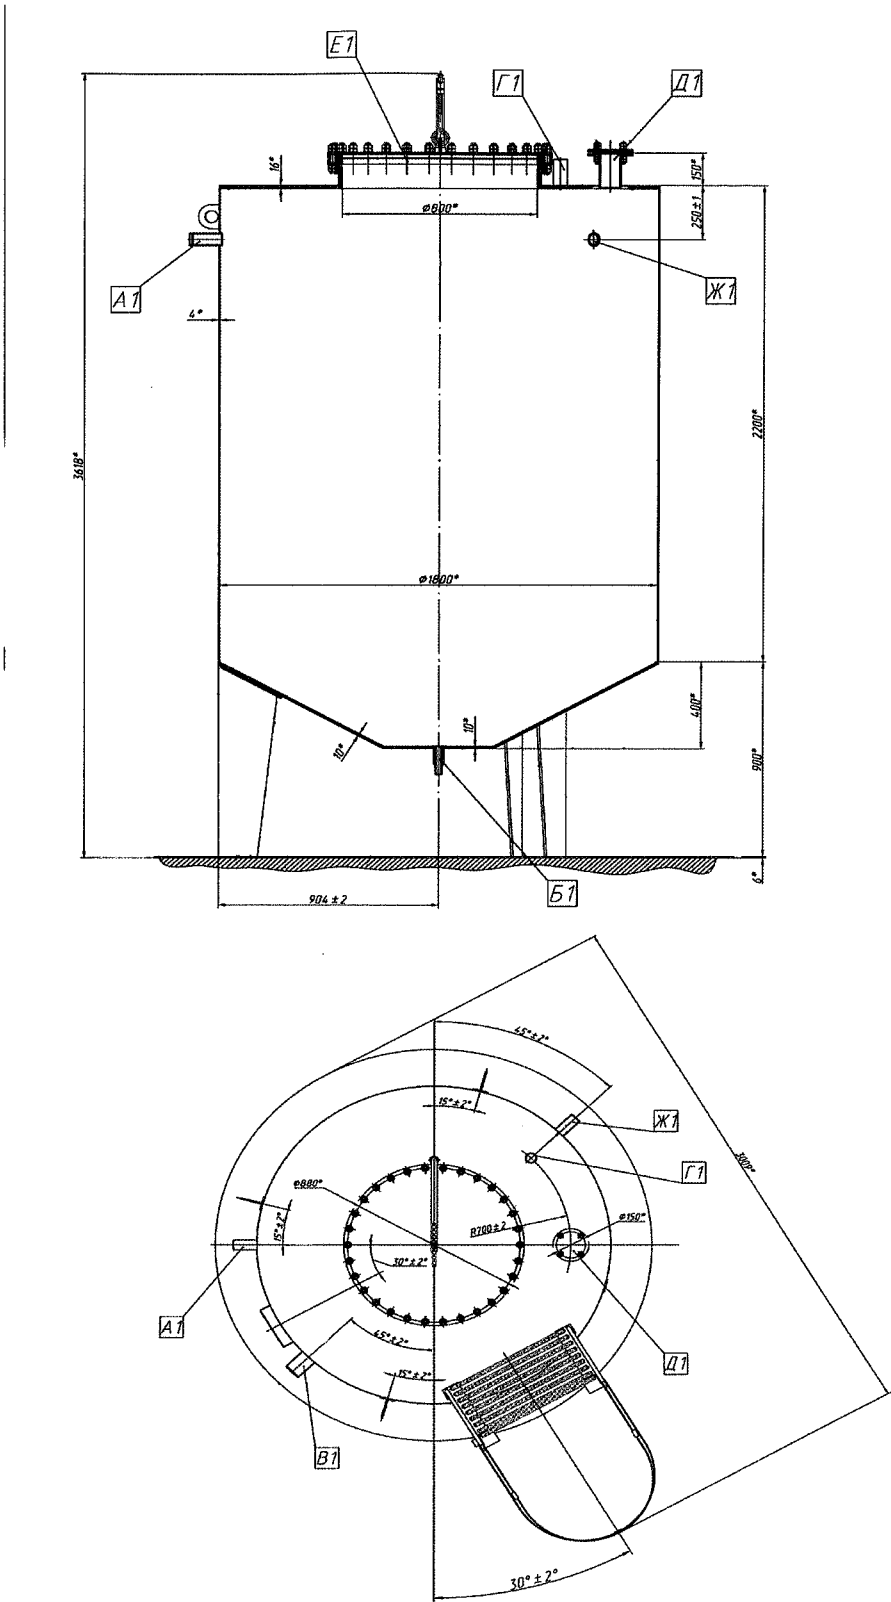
Габаритный чертеж мерника этаноламина LDN20BB001, LDN20BB002
